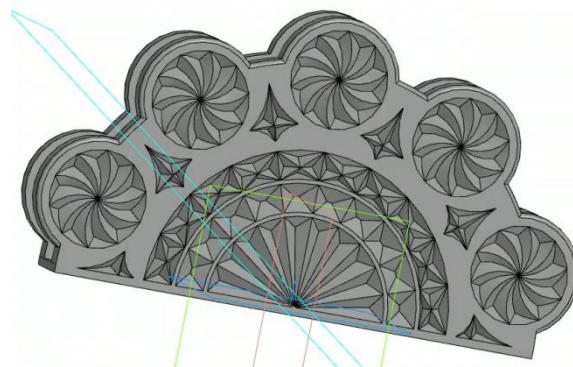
3D-модель подставки для салфеток с геометрической резьбой
